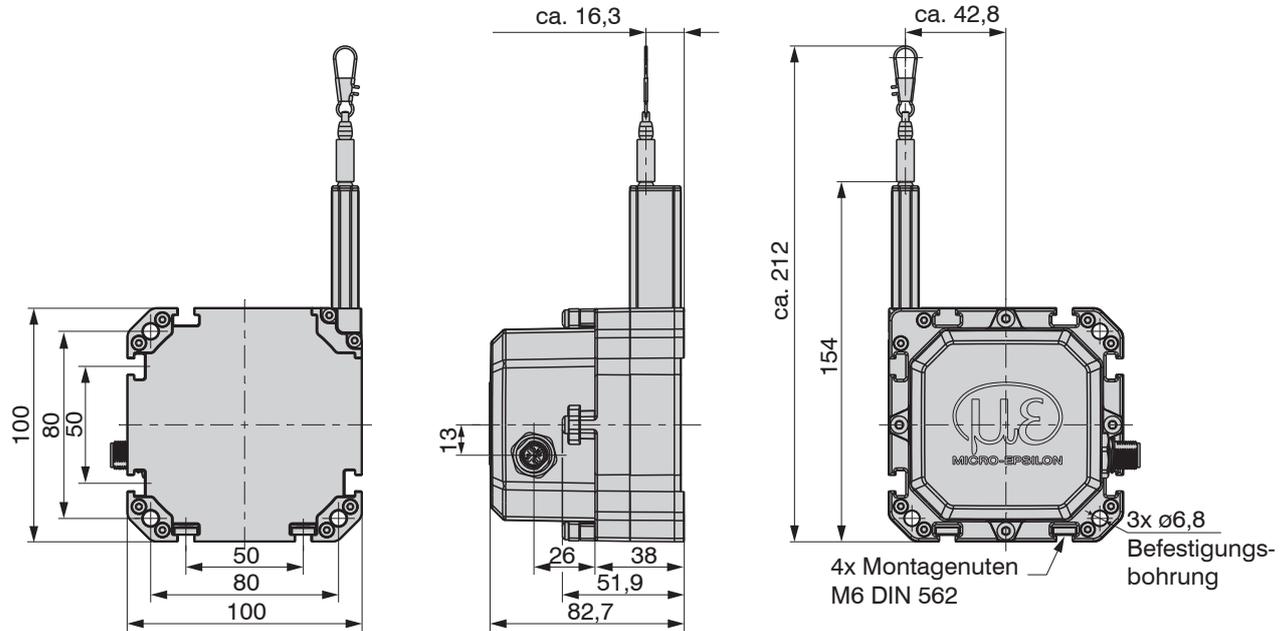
Maßzeichnung, WPS-3500-K100, WPS-5000-K100, WPS-8000-K100 mit Steckverbinder 5-polig M12x1, Abmessungen in mm
